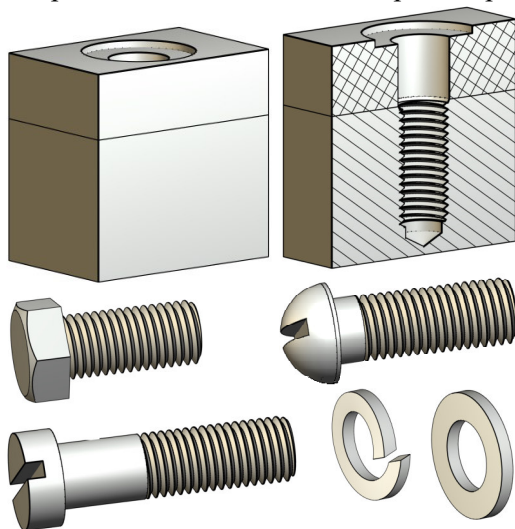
Иллюстрация к выбору стандартных резьбовых изделий для осуществления соединения
